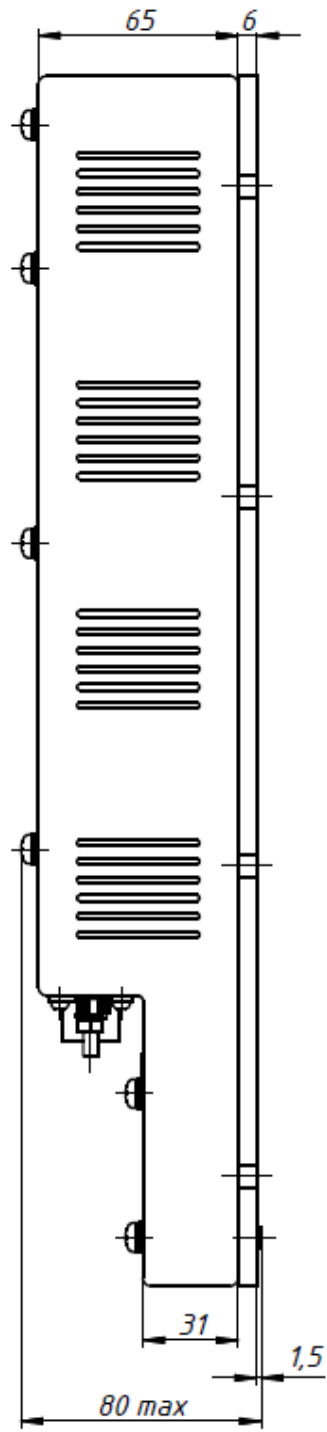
Габаритный чертёж видеомонитора в исполнении
